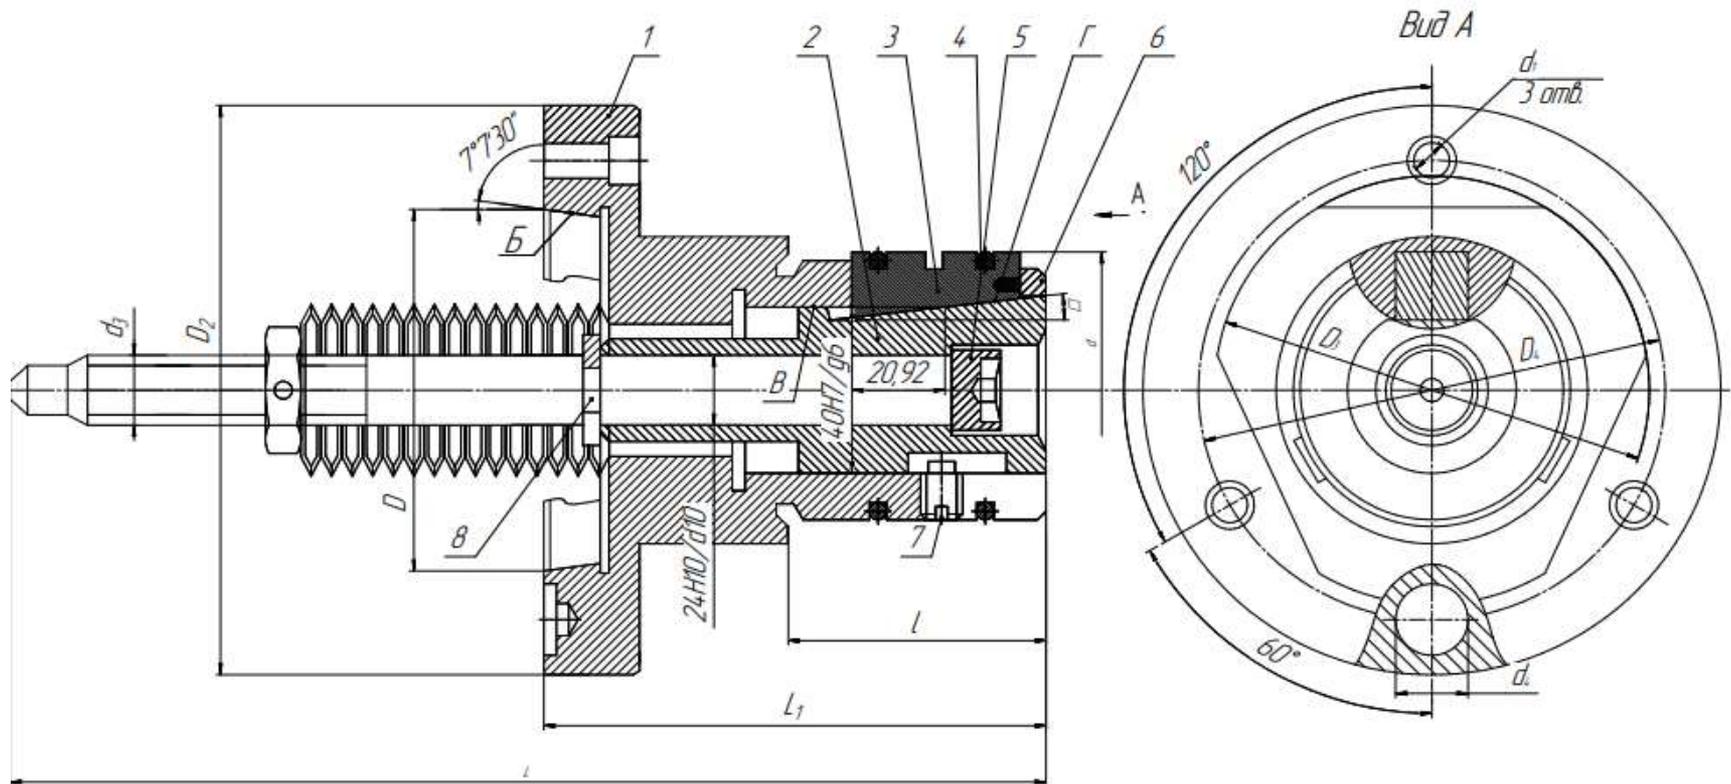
Пример ошибок при подготовке сборочного чертежа
